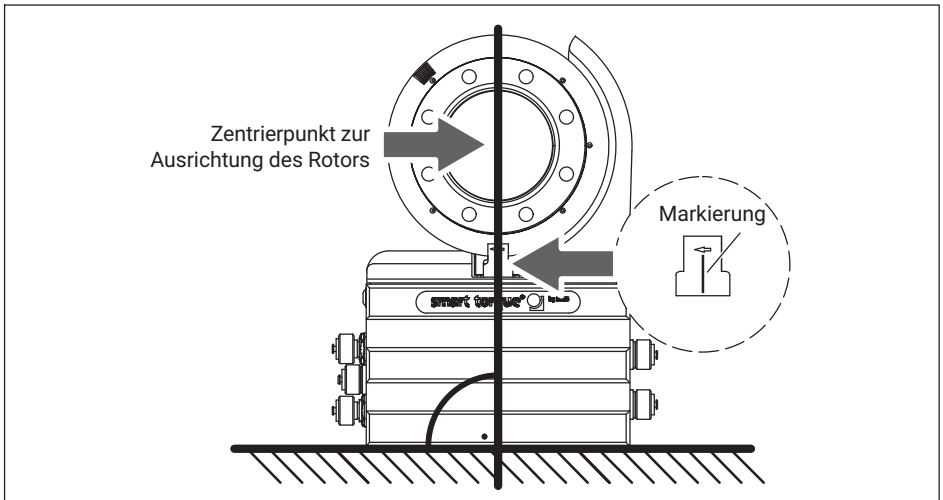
Ausrichtmarkierungen Rotor/Stator
